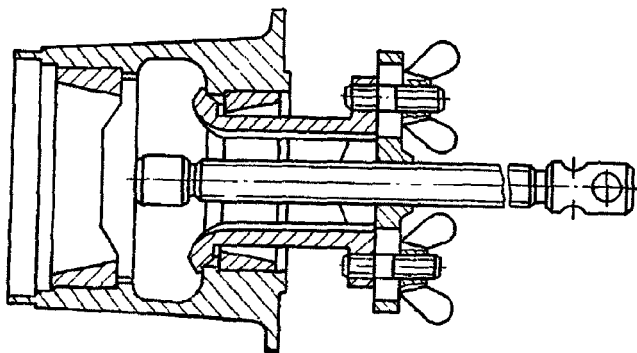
Приспособление для выпрессовки наружных колец подшипников ступиц переднего и заднего колес
